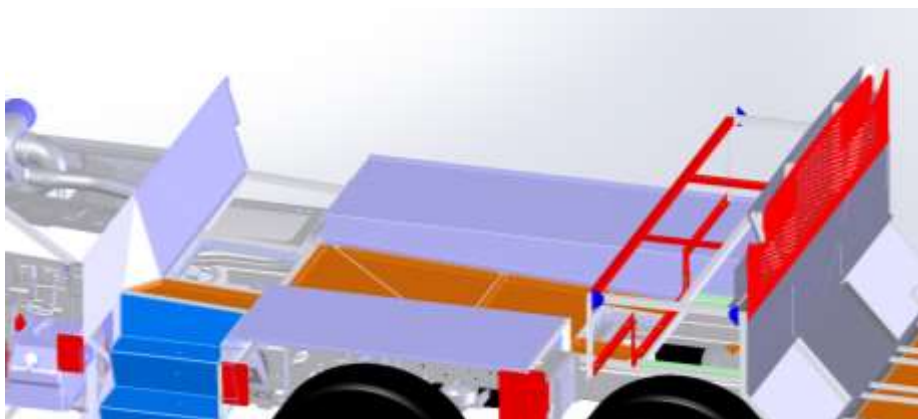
Imagem zona de aplicação de chapas da bagageira em 3D
